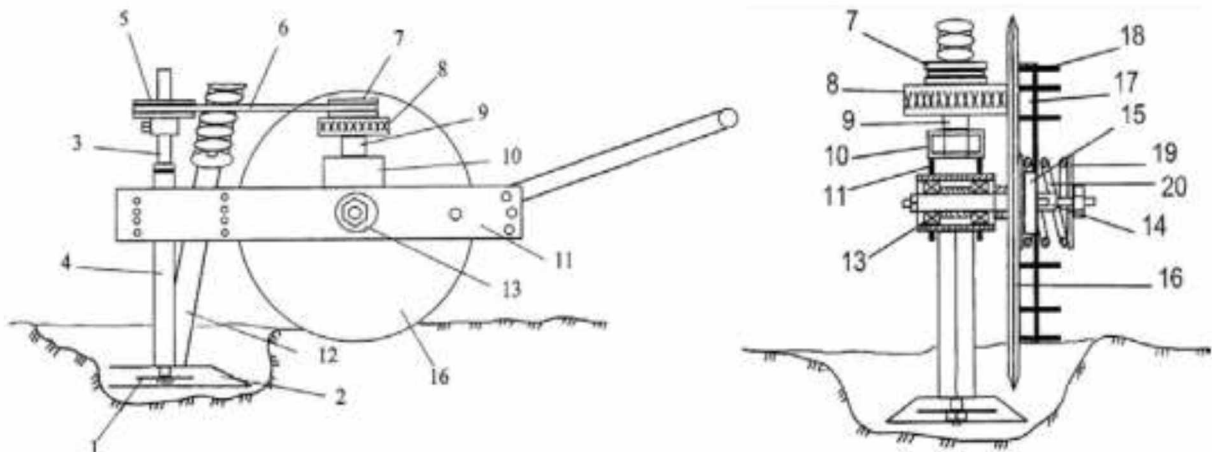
Леміш для всередині ґрунтового розкидного посіву: 1 - розкидальний диск; 2 - ніж; 3 - вертикальний вал; 4 - порожниста стійка; 5 - ведений шків; 6 - клиновидний ремінь; 7 - провідний шків 8 - каток; 9 - вісь; 10 - труби; 11 - пластинчасті повідці; 12 - трубчастий насіннепровід; 13 - корпус; 14 - валик; 15 - маточина; 16 - приводний диск; 7 - обмежувальне кільце; 18 - ґрунтозачеп; 19 - шайба; 20 - спіральна пружина
